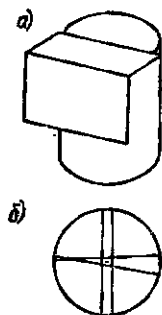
Разметка центрального отверстия в торце цилиндрической детали
